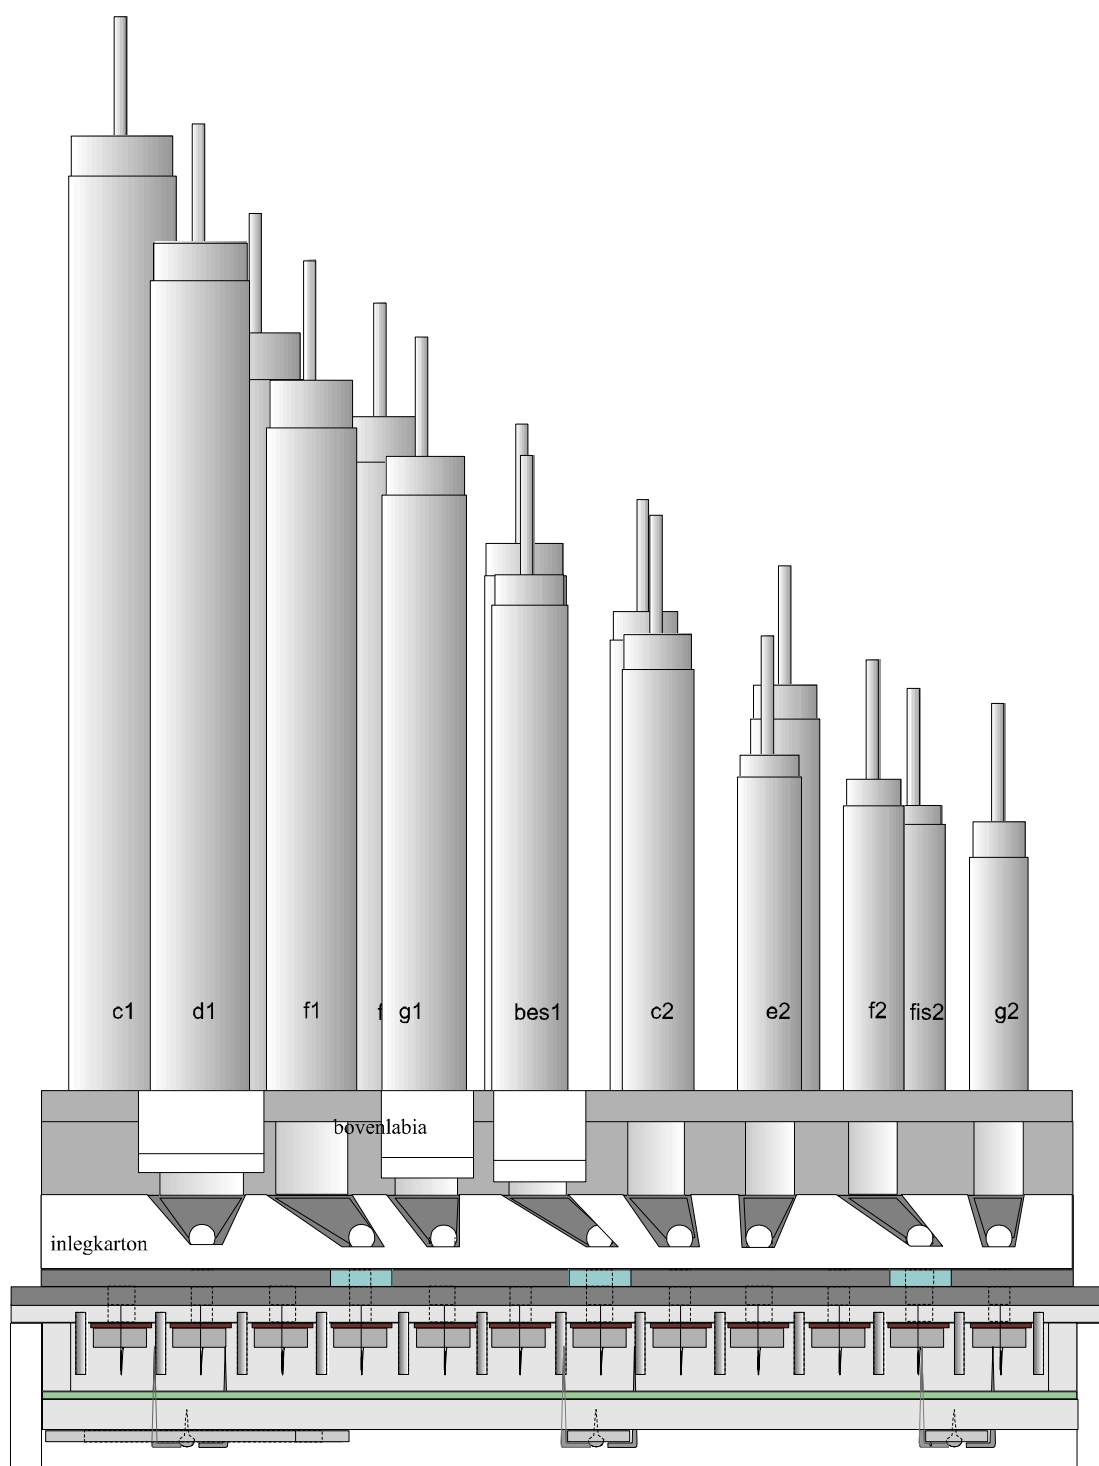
Vooraanzicht zonder enkele bovenlabia, voorstellen, voorzijde windkast en klavier
